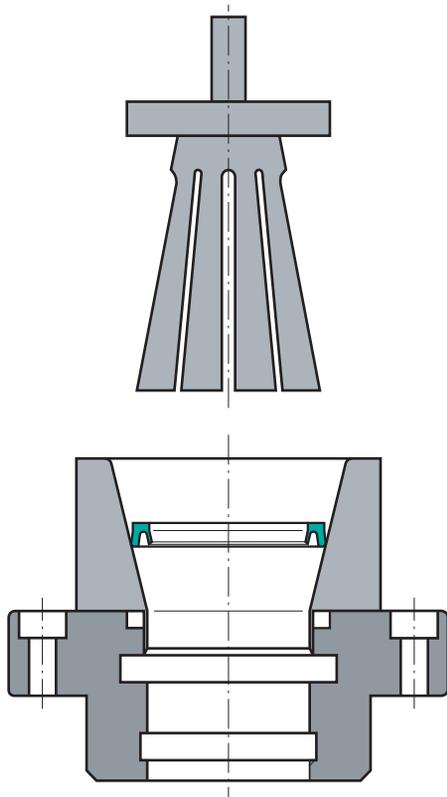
Útil de montaje 1 para juntas de vástago.
